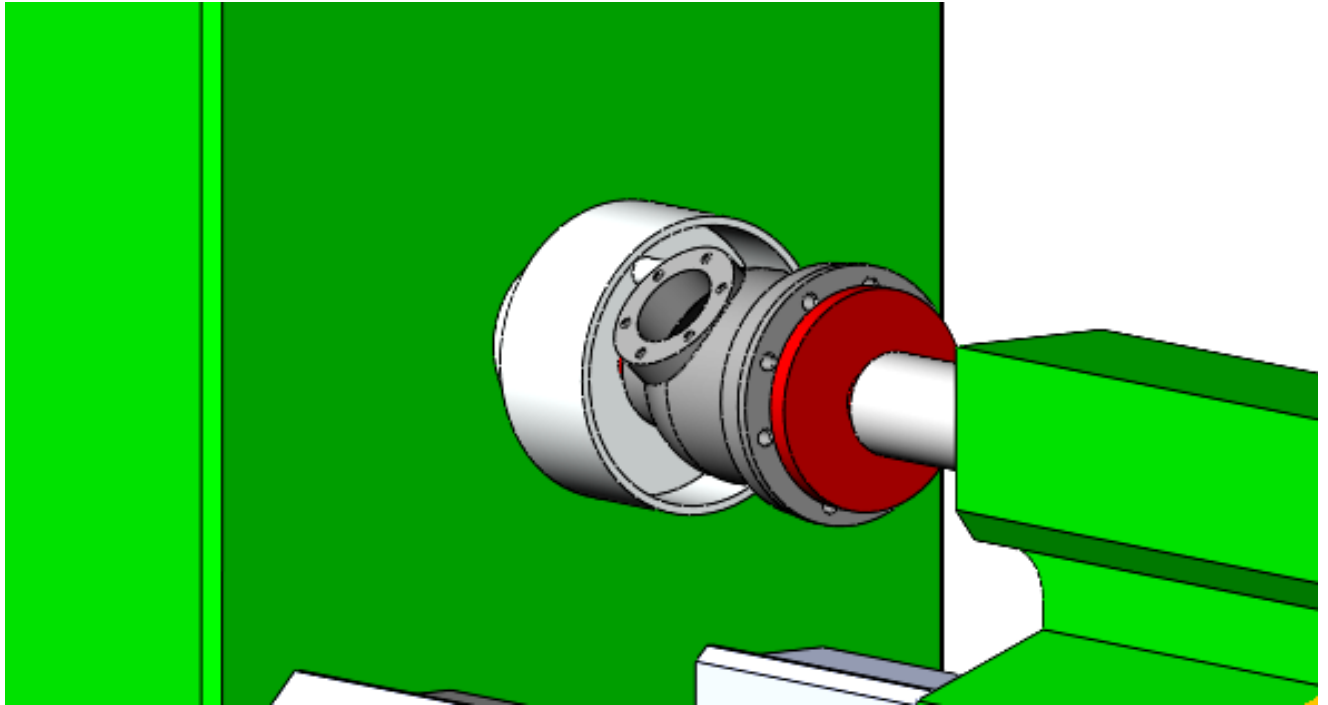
Теоретична схема базування обробки комплекту поверхонь 4.
